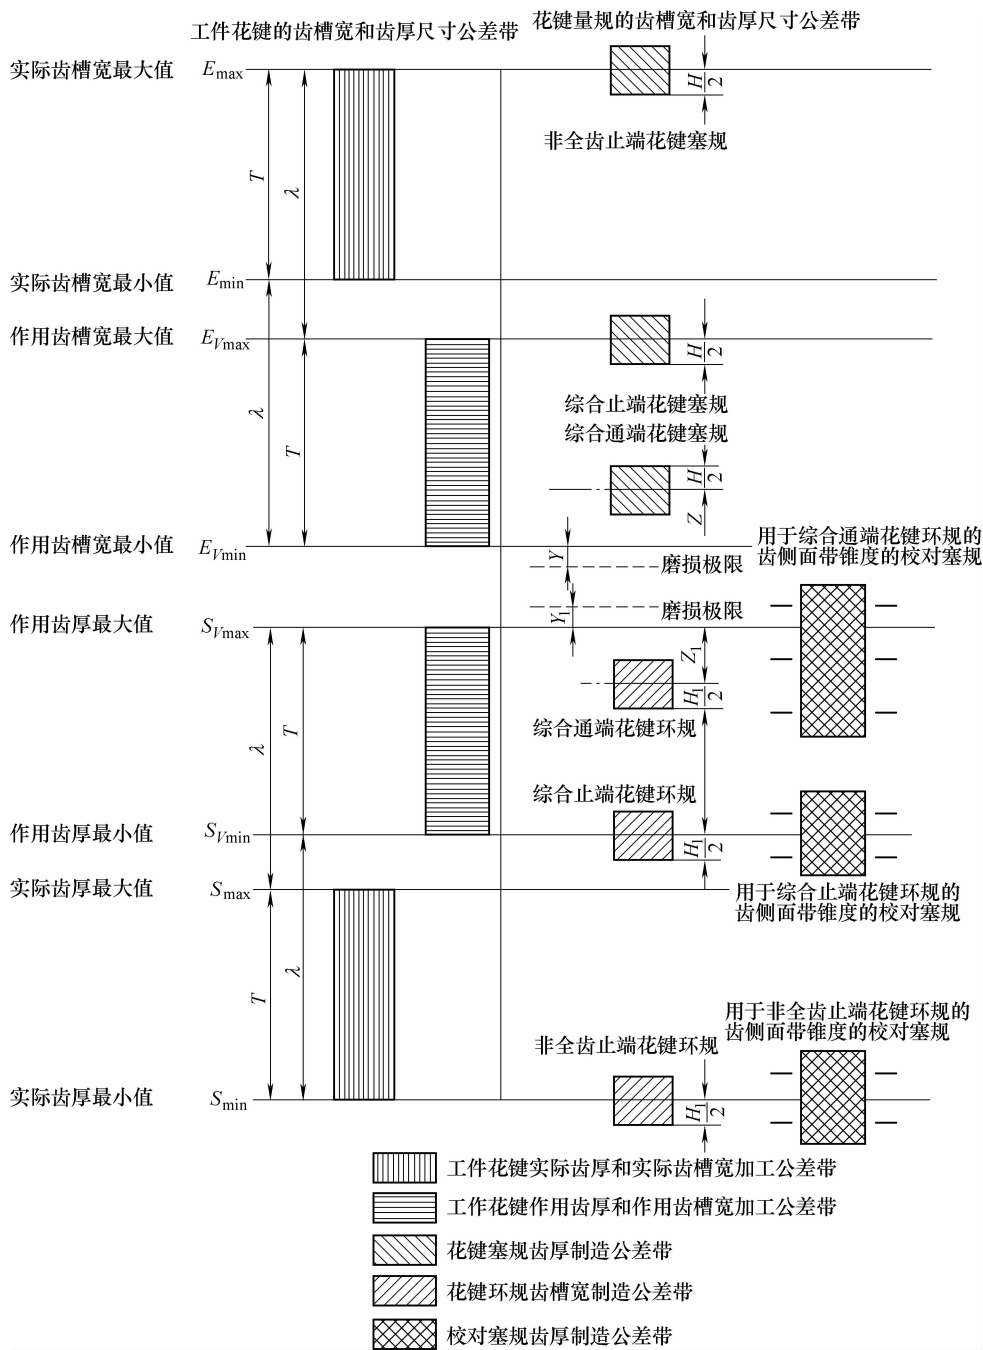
圆柱直齿渐开线花键塞规的齿厚和花键环规齿槽宽尺寸公差带
